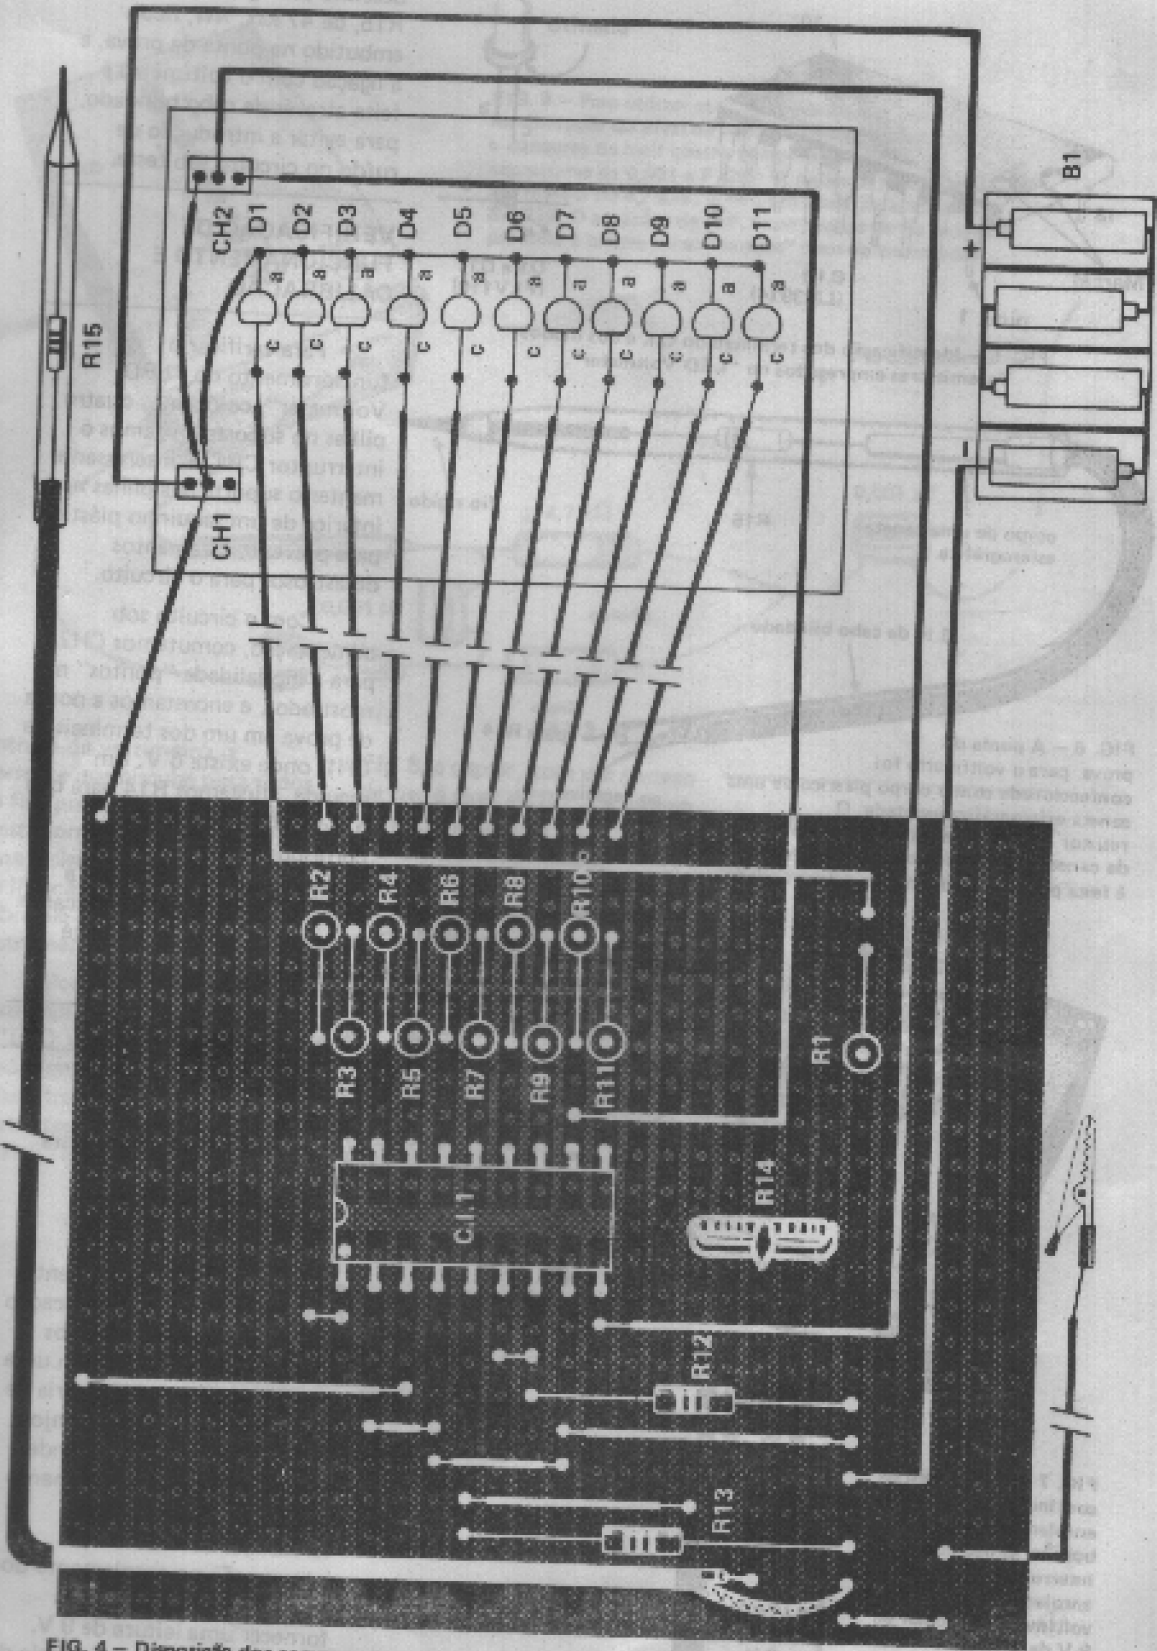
Disposiçao dos componentes sobre a plaqueta da Fig. 3, e ligaçao desta aos componentes externos.
